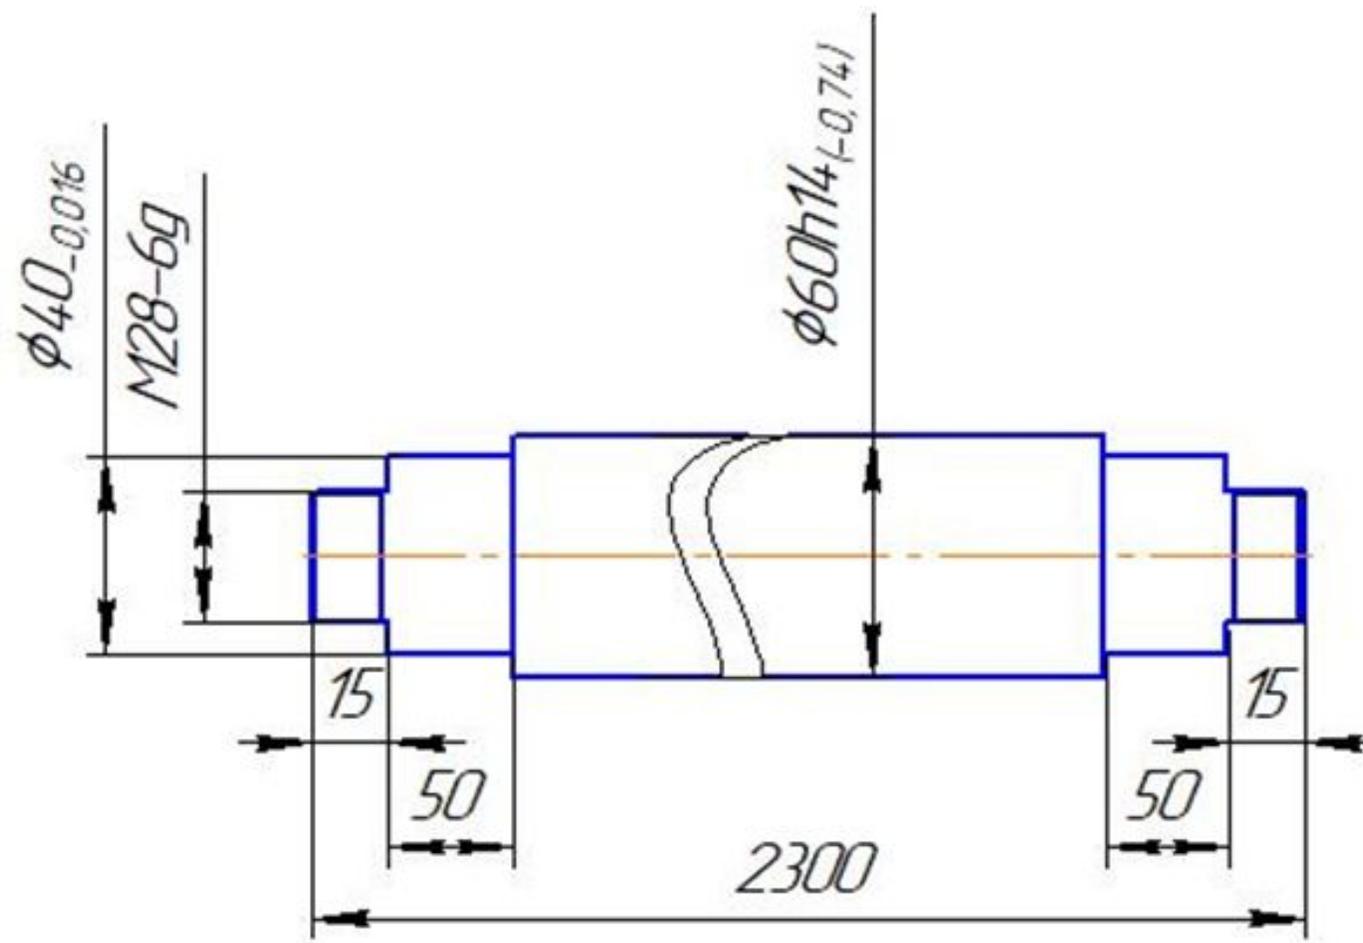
Эскиз вала катка зубчато-кольчатого ККЗ-6
